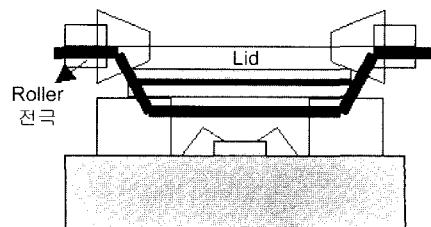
통전에 의한 package와 Lid간의 용접원리
